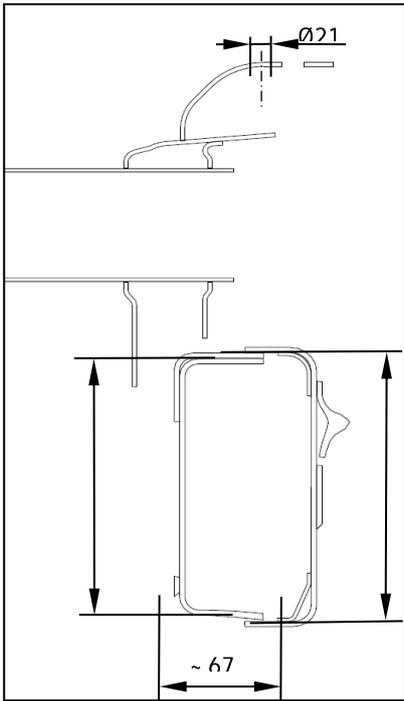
coupe Q-Q (Amarok SC)
